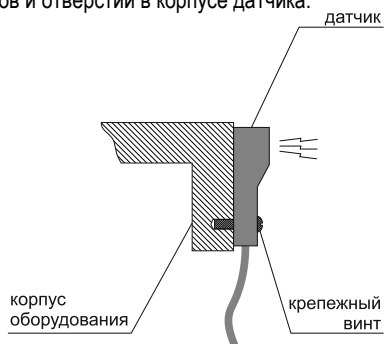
Установка датчика с торцевым расположением чувствительной поверхности
